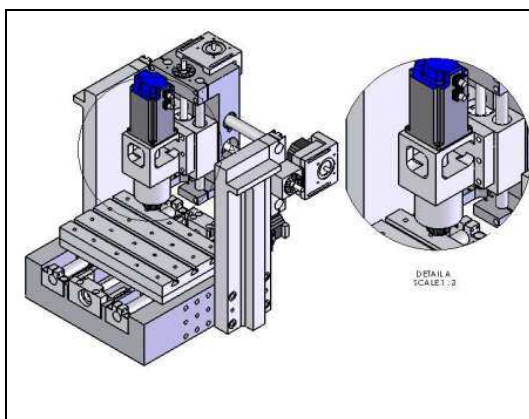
y 13: Dibujo por Ordenador de Pequeño CNC y Pequeño Equipo CNC
